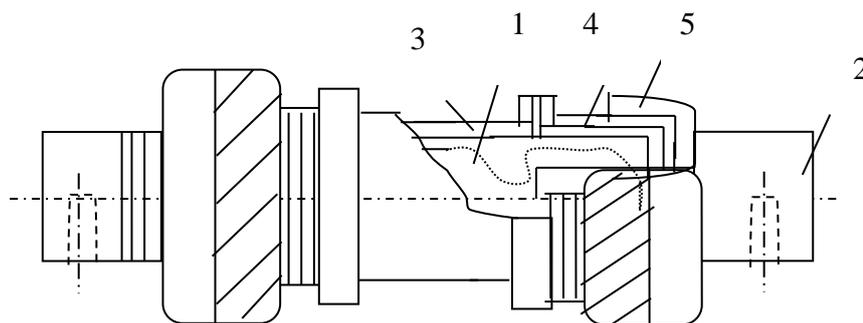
Предохранитель типа ПР-2: 1 – плавкая вставка, 2 – контактные ножи, фибровый цилиндр (3), латунная обойма (4), латунный колпачок (5) герметичного трубчатого патрона.
